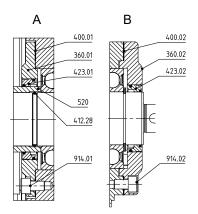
Ausführung Lagerträgerabdichtung mit Labtecta
